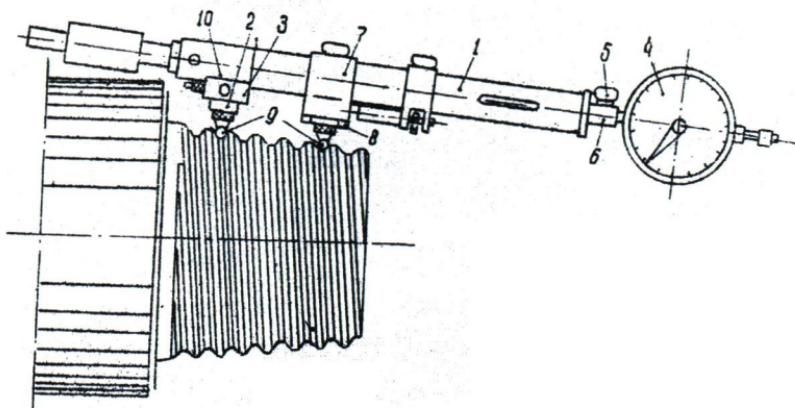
Проверка шага резьбы шагомером ШИ
